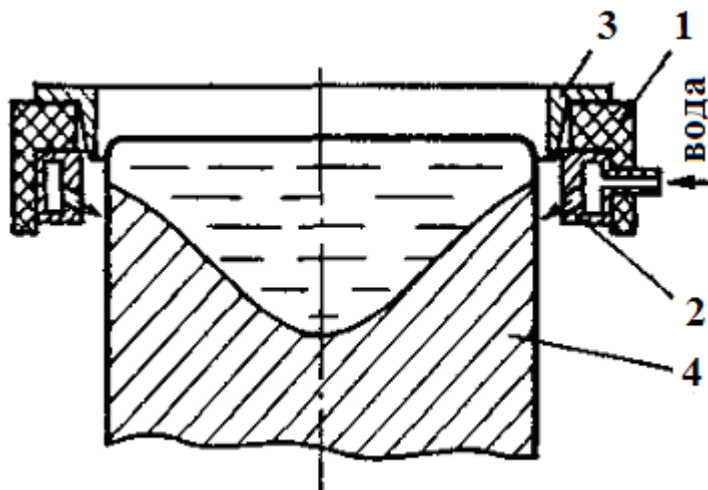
Схема электромагнитного кристаллизатора для отливки плоских и круглых слитков: 1 – корпус; 2 – индуктор; 3 – экран; 4 – слиток
